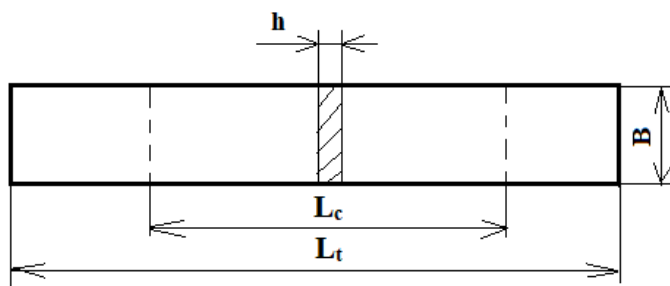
Forma și dimensiunile epruvetei pentru încercarea la încovoiere.
